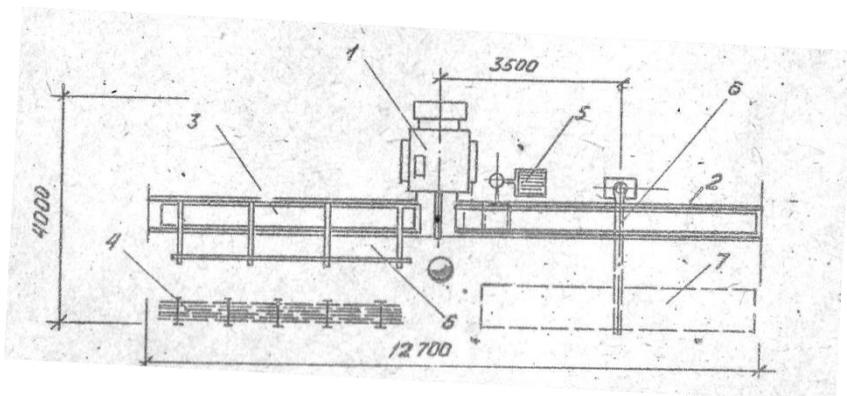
Схема организации сварки тяжелых плоских каркасов:
